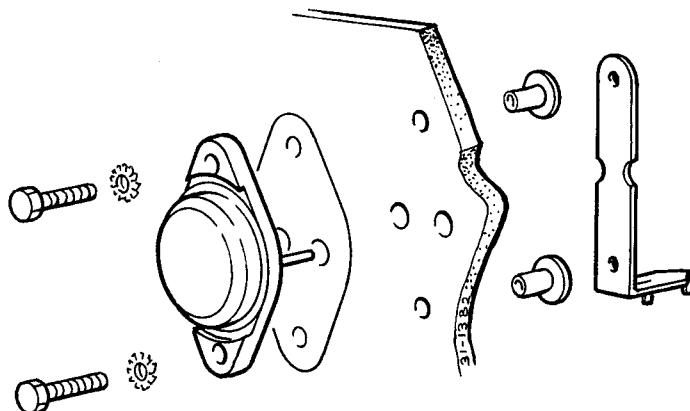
Montering av slutt-transistor, husk silikonfett på begge sider av glimmerskiven.
